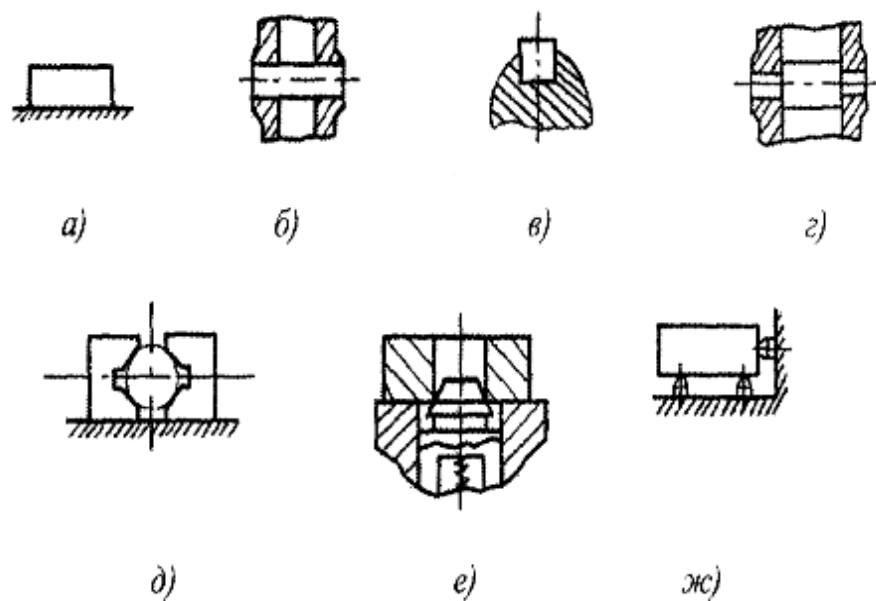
Види баз: а – площа, б – циліндр, в, г – сукупність поверхонь, д – вісь, е – коло, ж – точка
